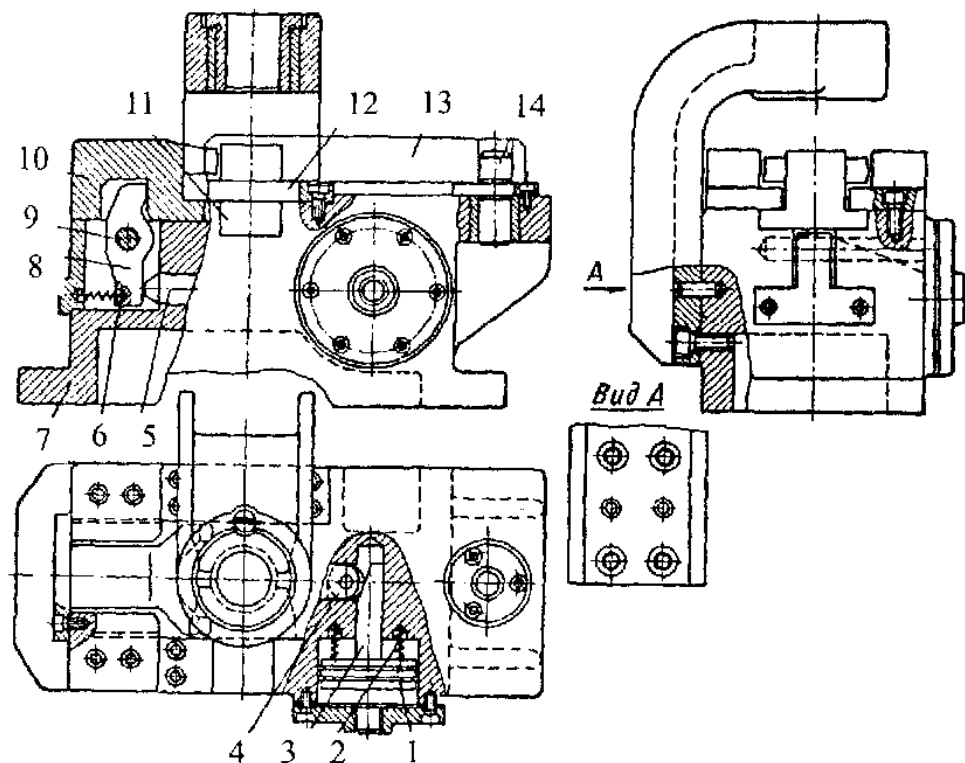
Стационарний пристрій з постійною кондукторною плитою і пневмоприводом
